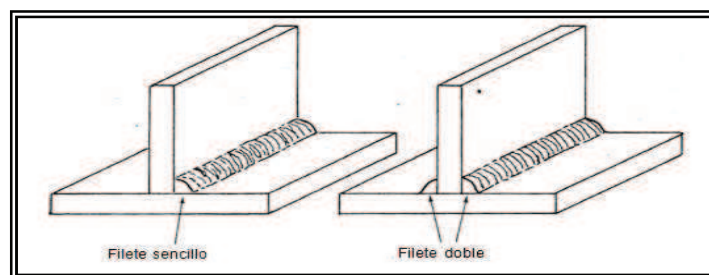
Soldaduras de filete sencillo y de filete doble.
